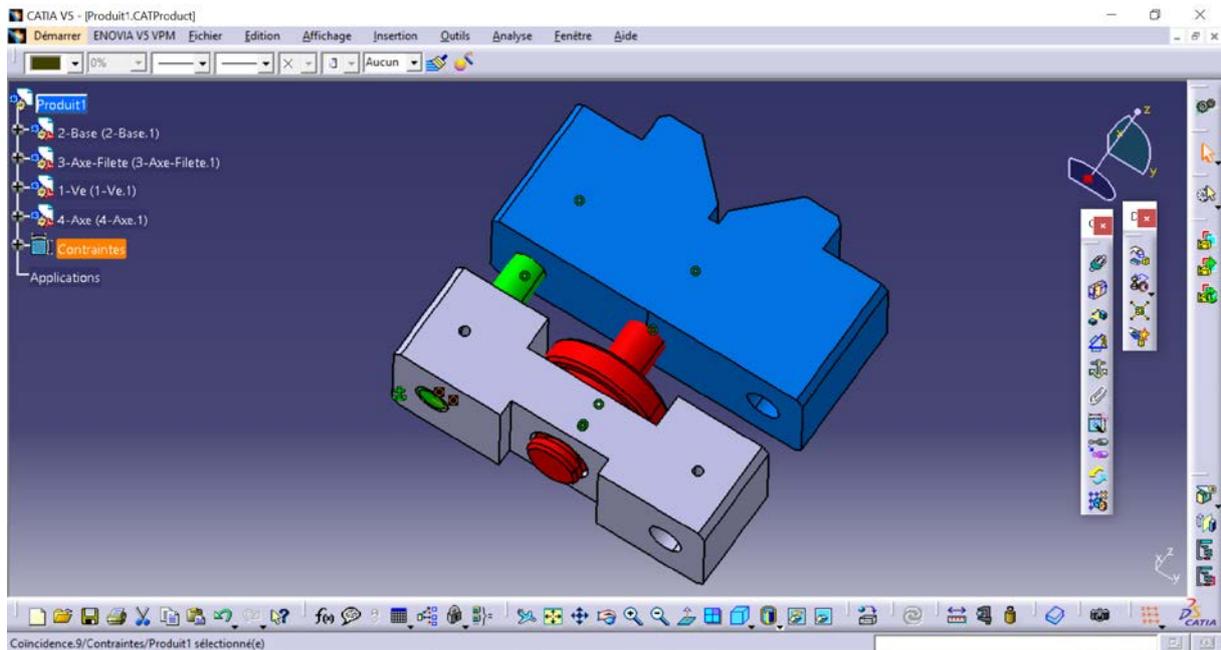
Assembly Design des Pièces 1, 2 et 4 (après mise à jour) [1], [2]
